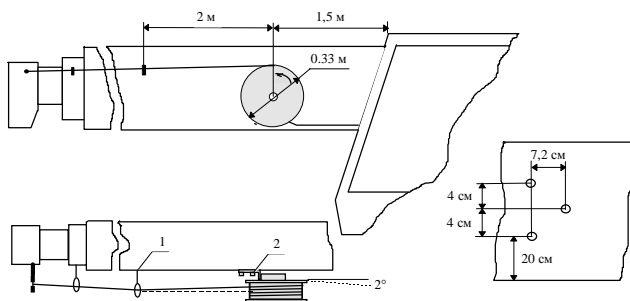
Установка датчика длины стрелы и разметка мест крепления
